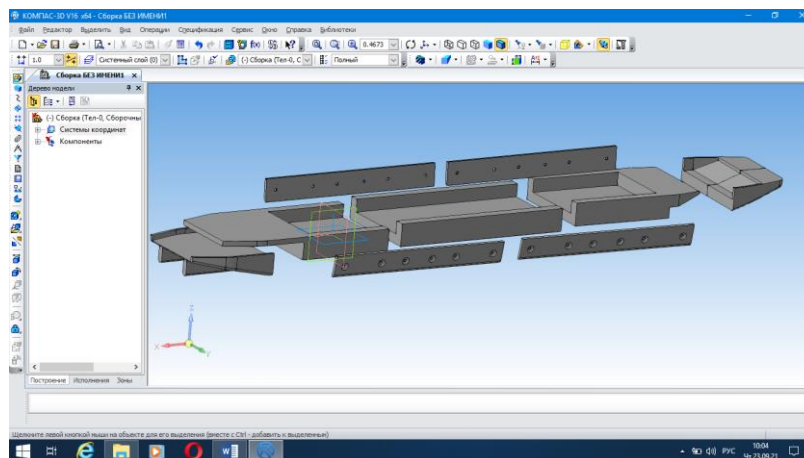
Процесс сборки основных элементов, носовой и кормовой частей 3D-модели НС
